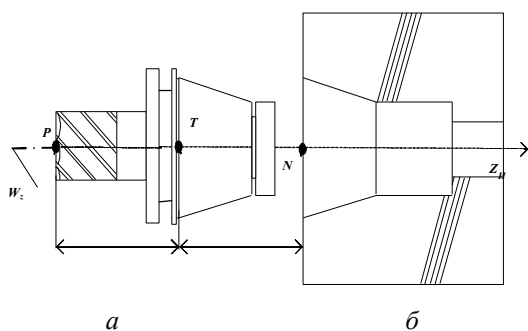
Схема базирования инструмента: а - инструментальный блок, б - элемент станка
